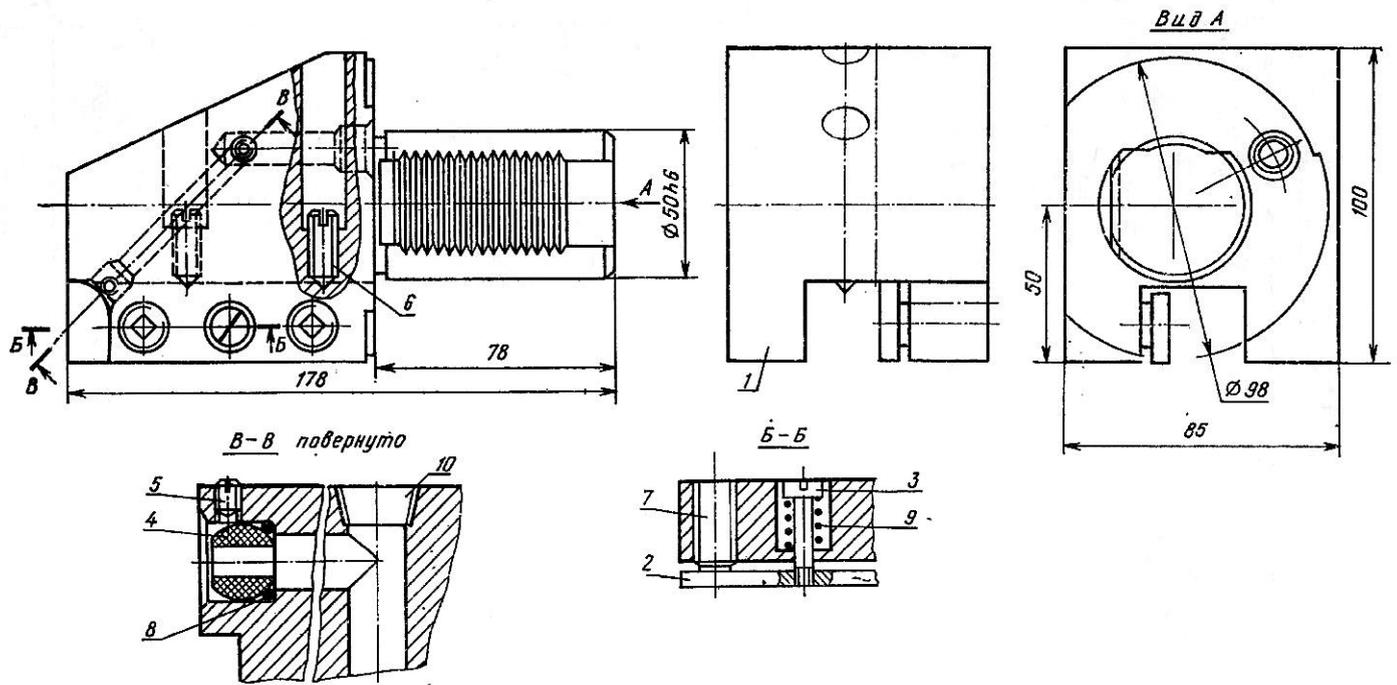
Резцедержатель с параллельным открытым пазом удлиненный 191.711.165;
